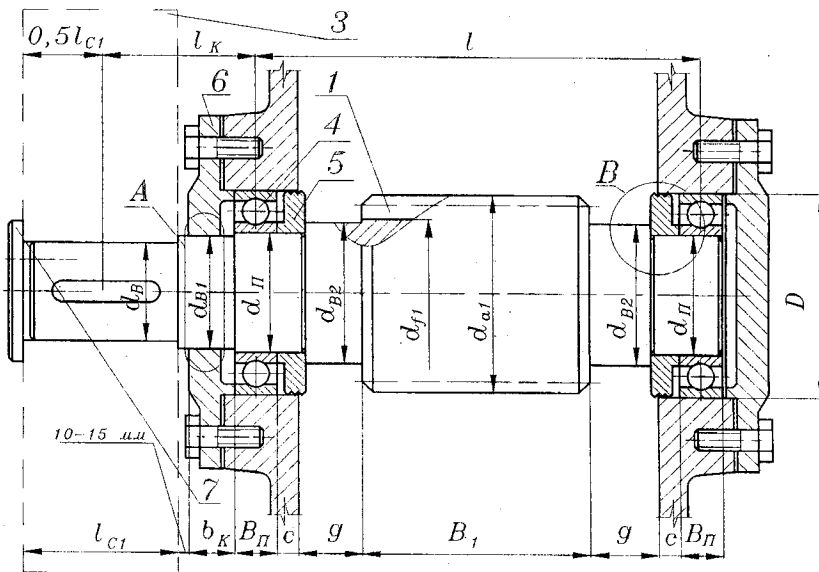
Вал-шестерня прямозубої циліндричної передачі
